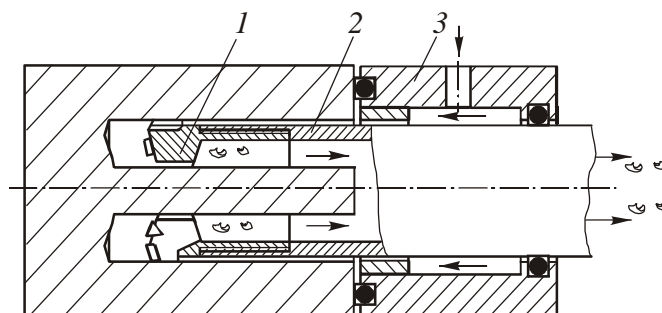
Схема обработки глубоких отверстий кольцевым сверлом БТА:
